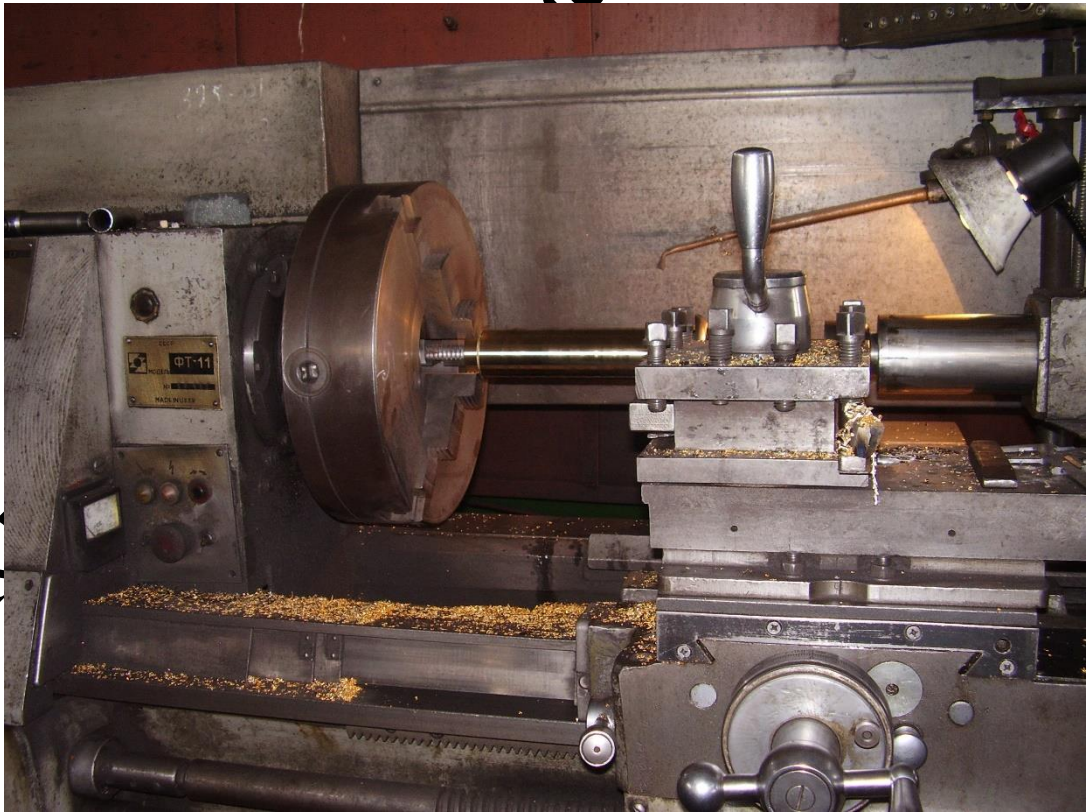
Обкатка вала із сталі 10X17H13M2Г з подачею ЗОР
